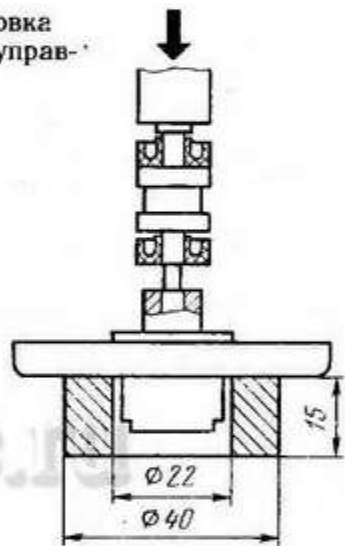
Напрессовка пластинчатой шайбы на клапан управления:
